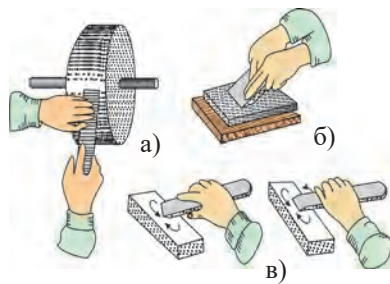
Заточка резца при подготовке рубанка к работе: а – на диске точильного камня; б – на оселке; в – на точильном камне.
